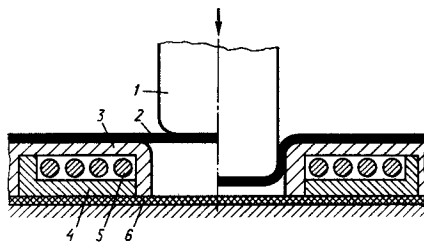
Схема штампа для рельефной формовки листовых заготовок с нагревом: 1 — пуансон; 2 — заготовка; 3 — матрица; 4 — электроннагревательная коробка; 5 — электроннагреватель; 6 — теплоизоляция
